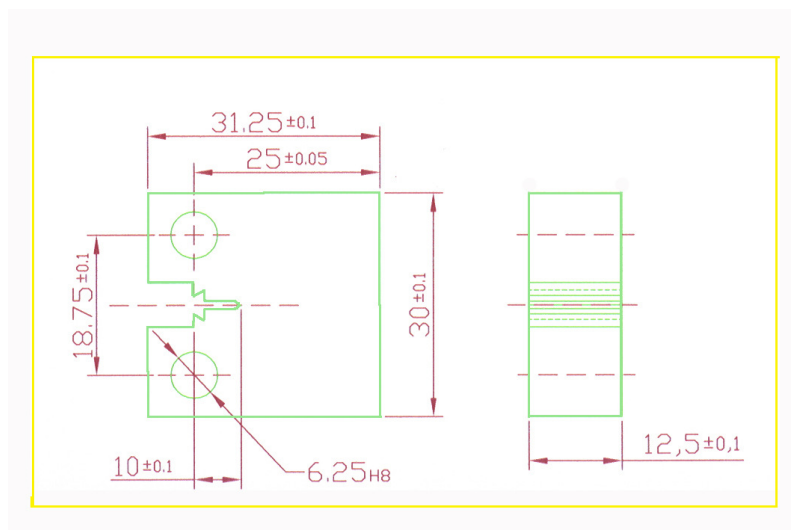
b: Desenho do corpo-de-prova C(T) das amostras usadas no projeto. Amostra de 1/2T tem integrado facas afiadas (dimensões em mm)
